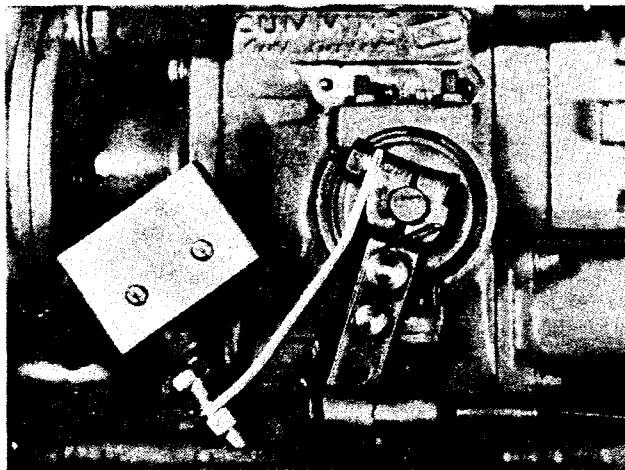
, (N12030J). Montaje del interruptor de la bomba de gasolina.
